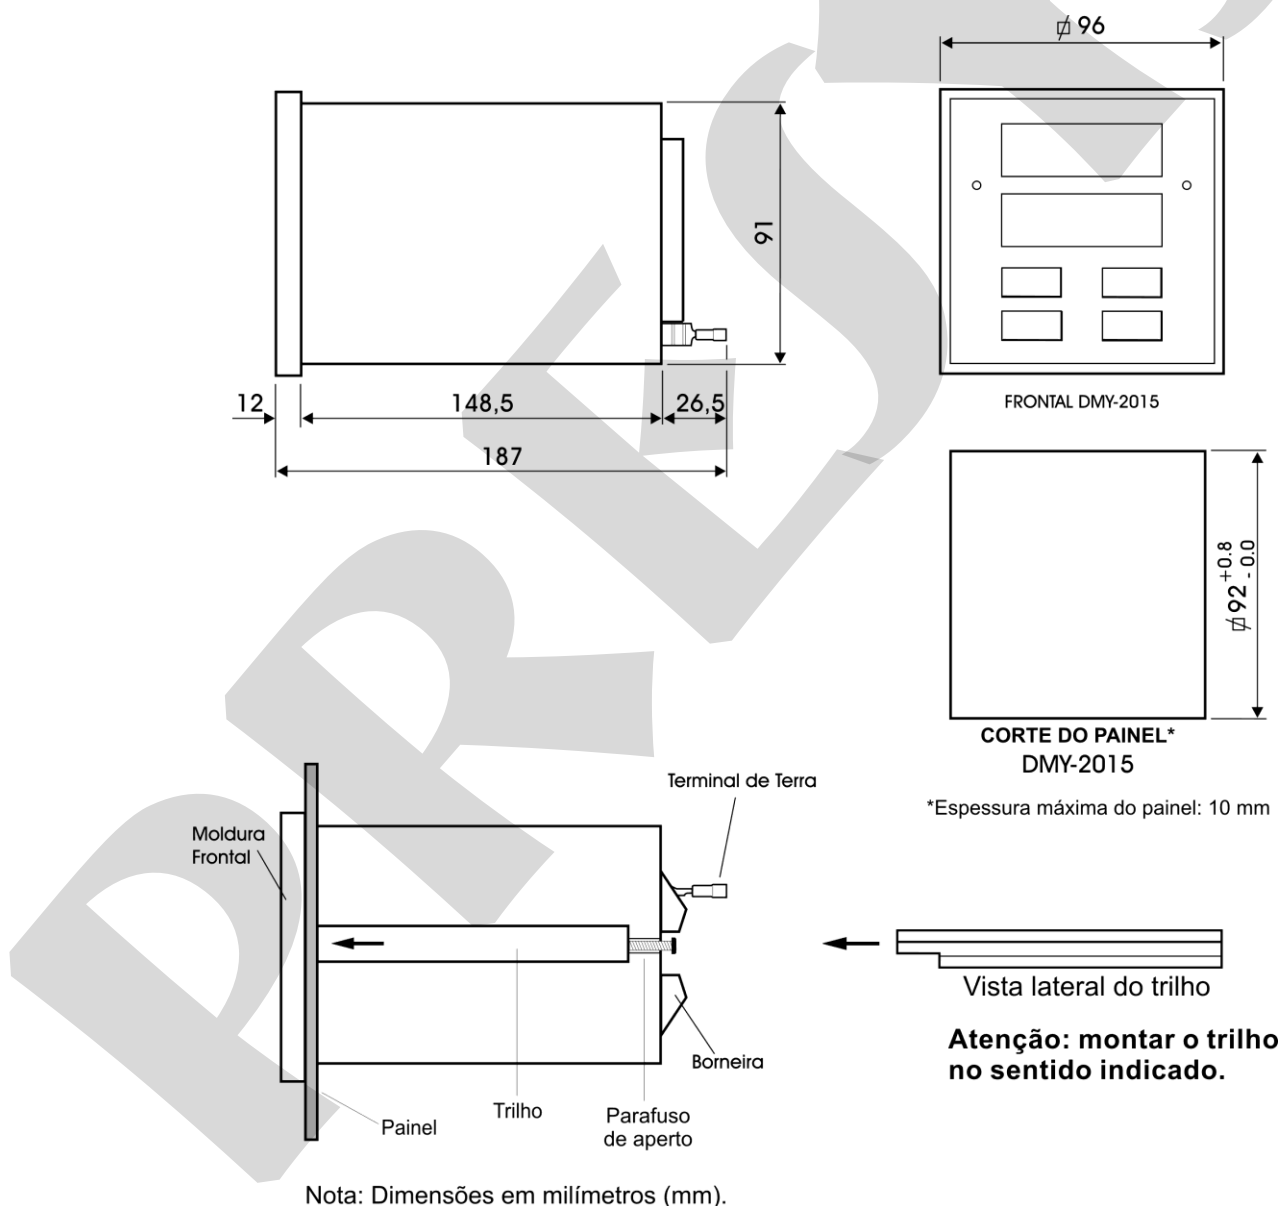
Desenho dimensional, corte e vista lateral da montagem no painel
